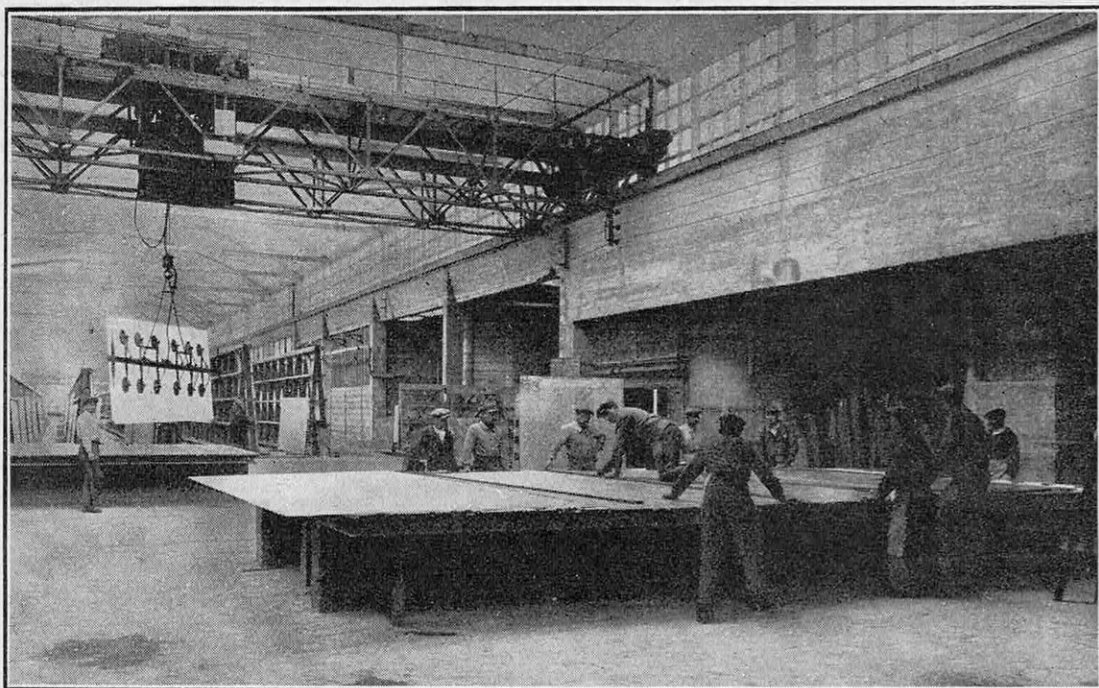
ÉQUARRISSAGE ET DÉCOUPAGE DES GLACES
